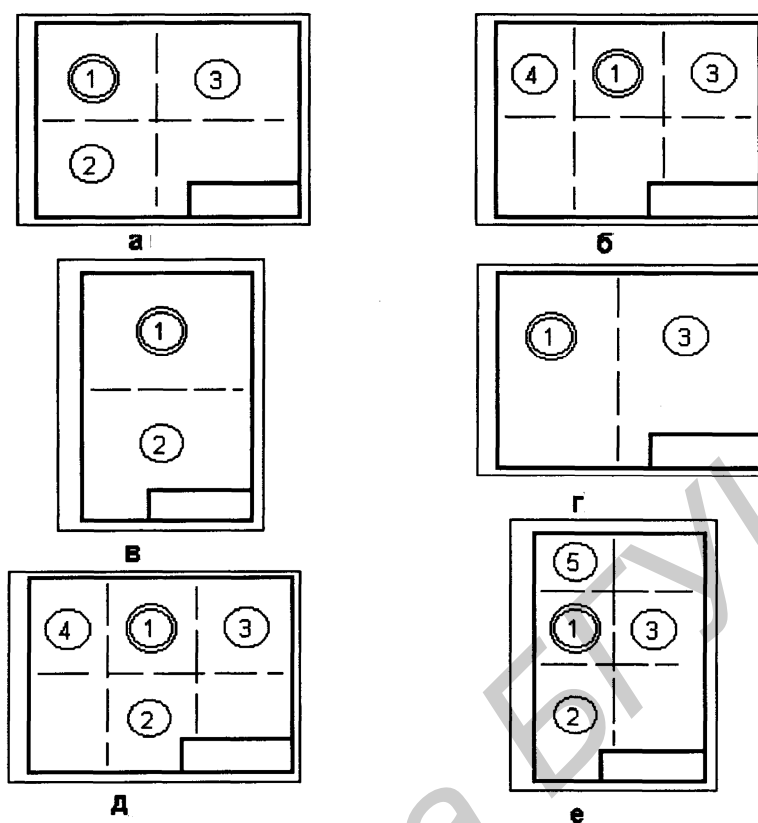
Варианты расположения видов на чертеже (а - е):
